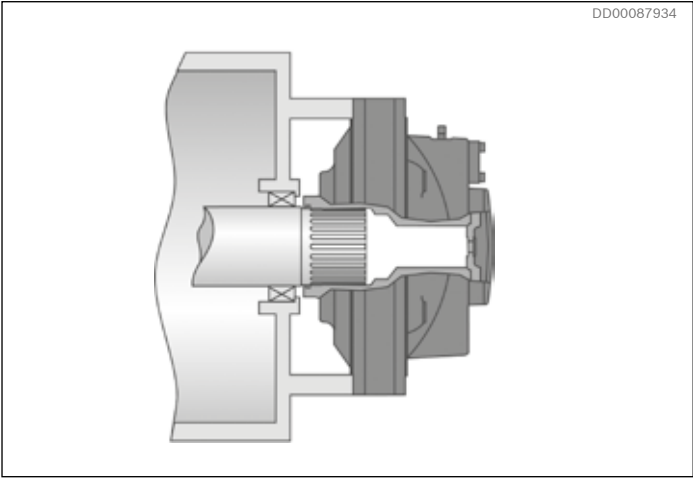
Motor instalado con brida con estrías y baja carga radial del eje accionado.
